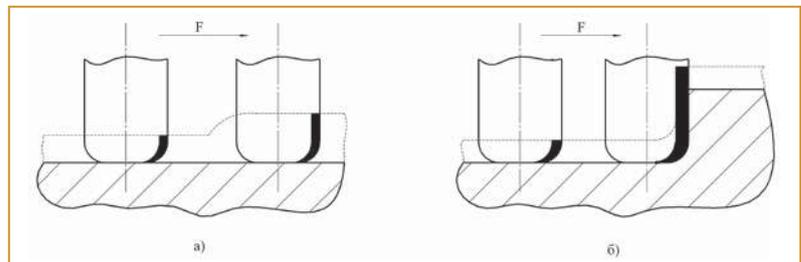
Примеры локального изменения охвата фрезы материалом заготовки
